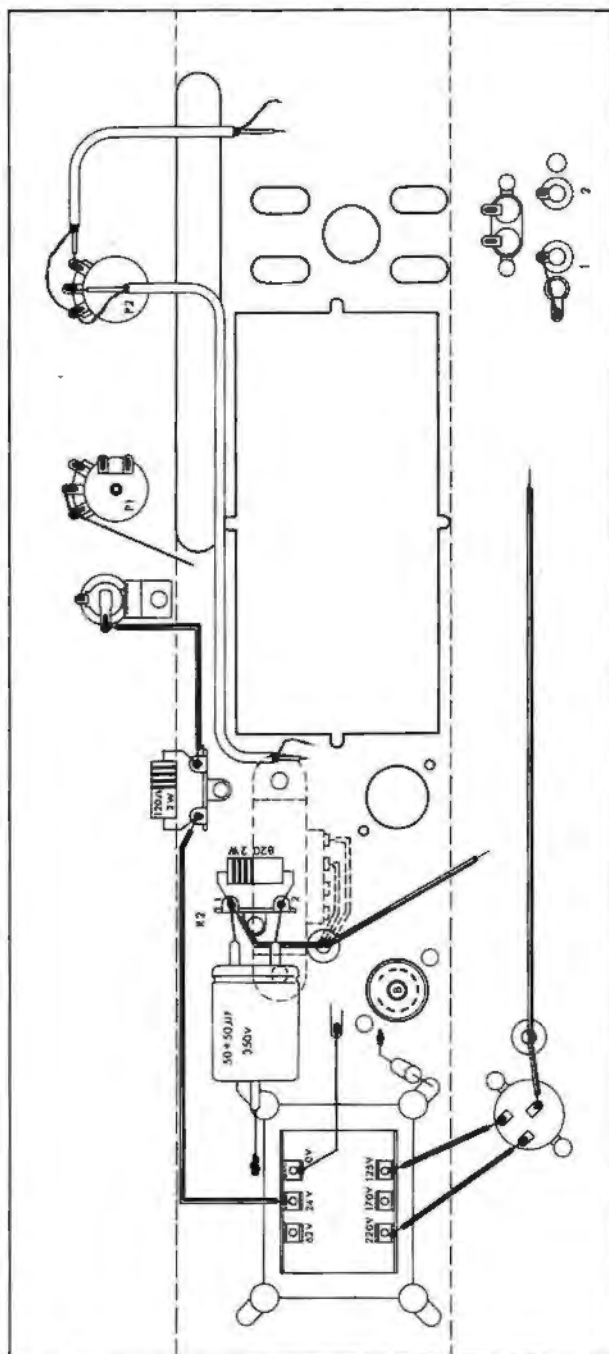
Disposición de los componentes que conserva el chasis para proceder a su nueva fase.
